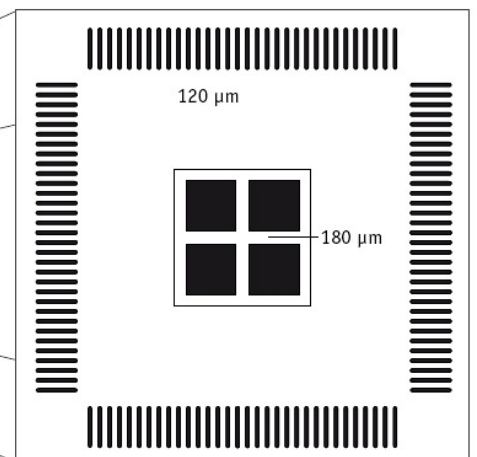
QFP-Bauteil mit Heat-Sink-Anschlüssen
